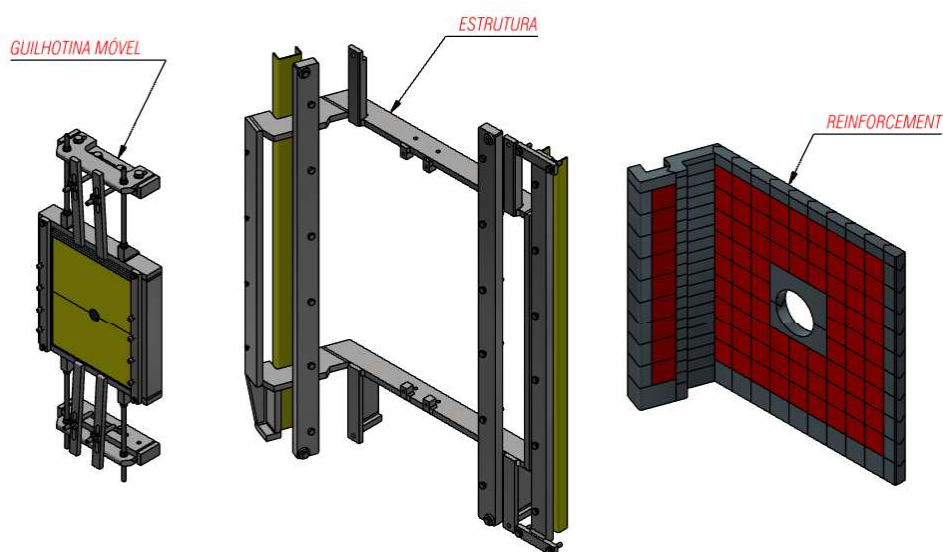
Estrutura básica de um conjunto de Guilhotina
